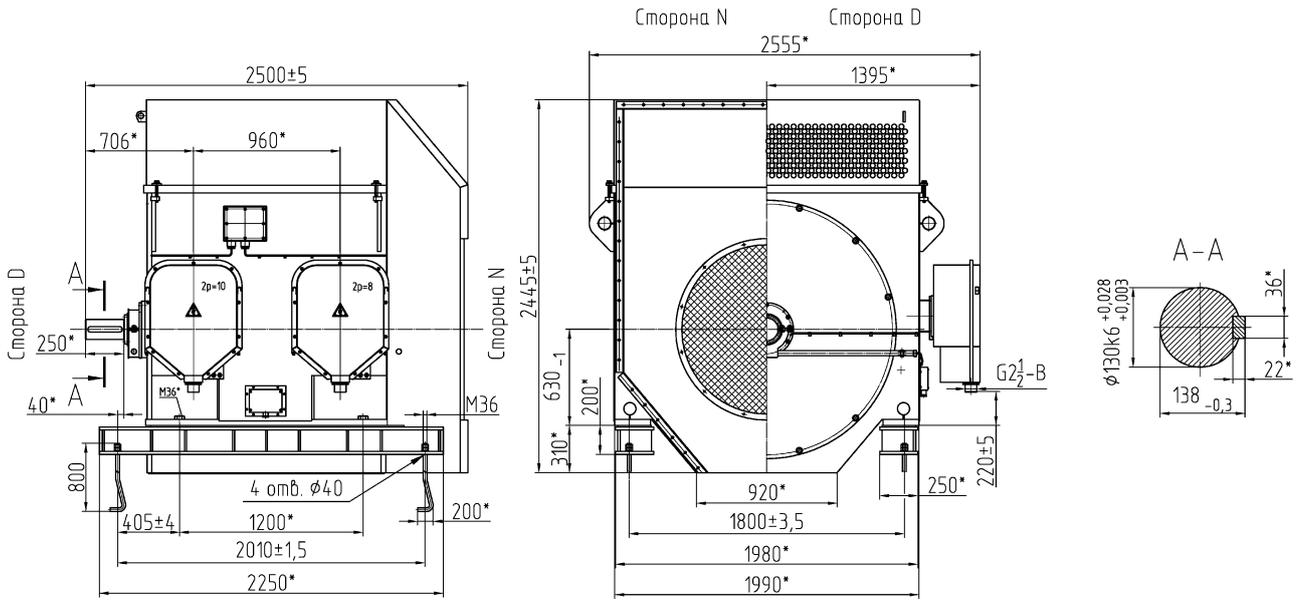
Габаритные и установочно-присоединительные размеры двигателей АОД-800/400-8/10У1 и АОД-1000/500-8/10У1
